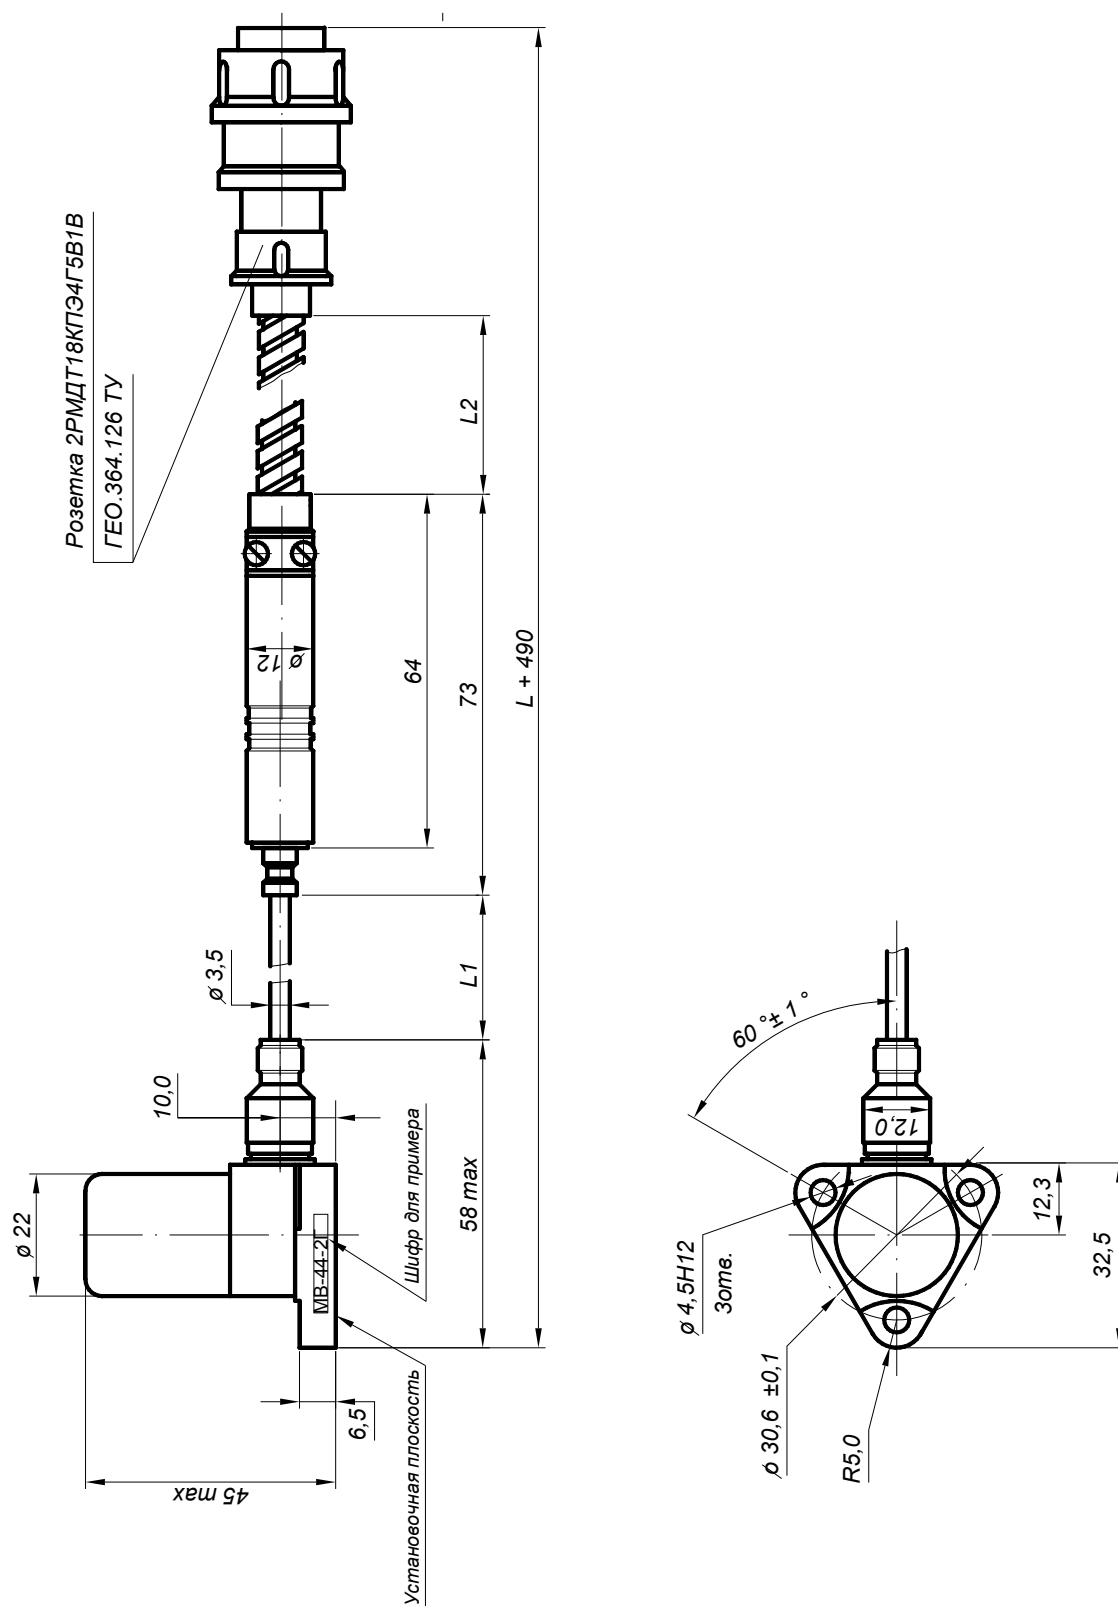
Габаритно-установочные размеры вибропреобразователя MB-44-2Г/L1/L2
